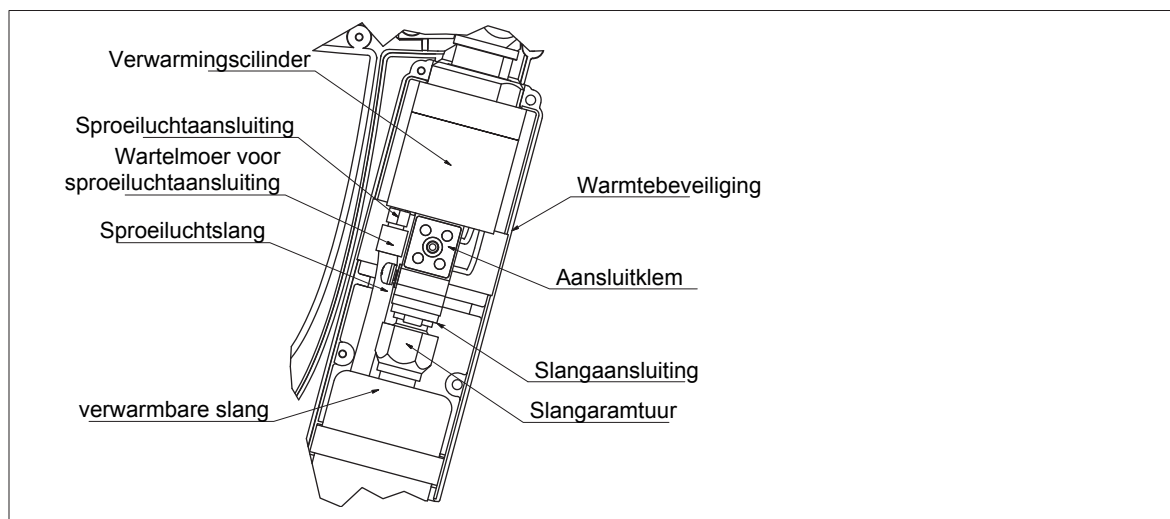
/7: Slangaansluiting in detail (version spray als voorbeeld)
